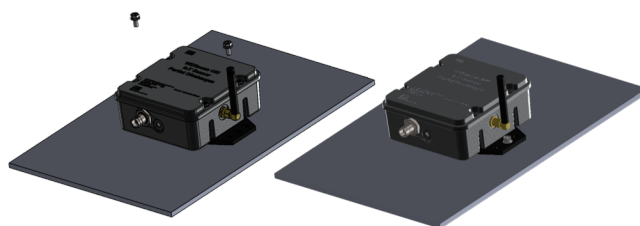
Montagem do conjunto de sensor com presilha para painel.
